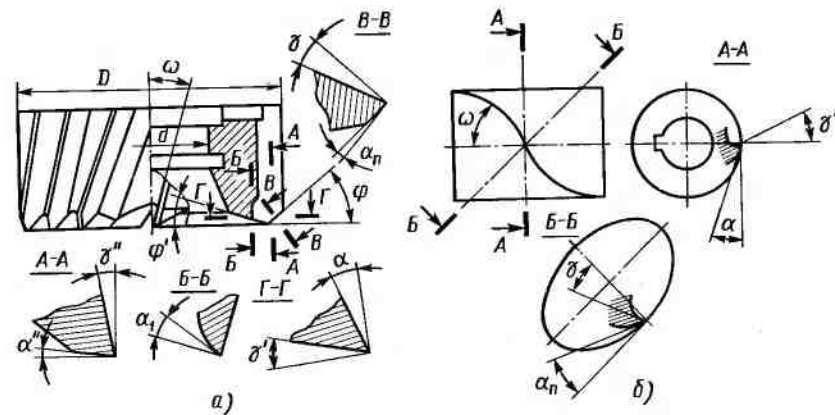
Геометрические элементы торцовой (а) и цилиндрической (б) фрезы
